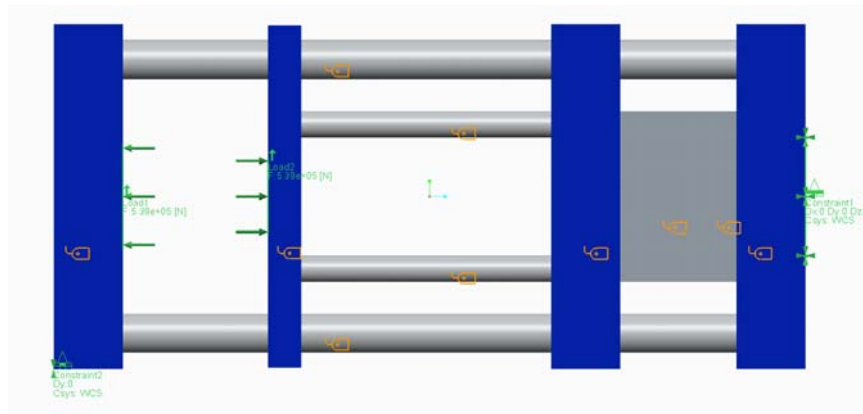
Máquina de inyección sometida a las condiciones del ensayo en vacío
